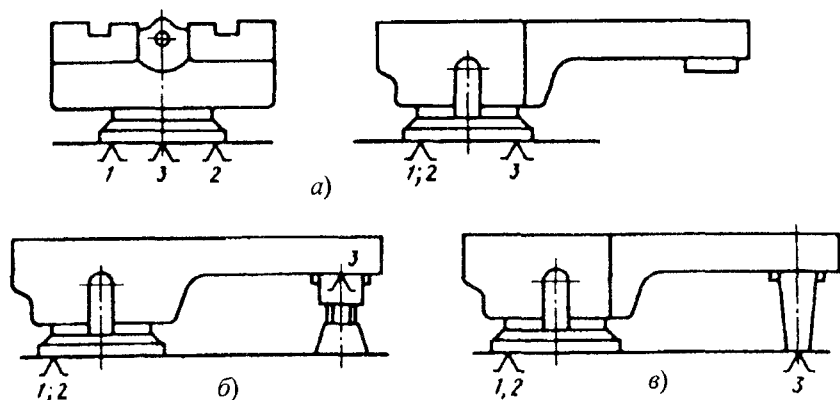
Схемы базирования каретки револьверного станка:
